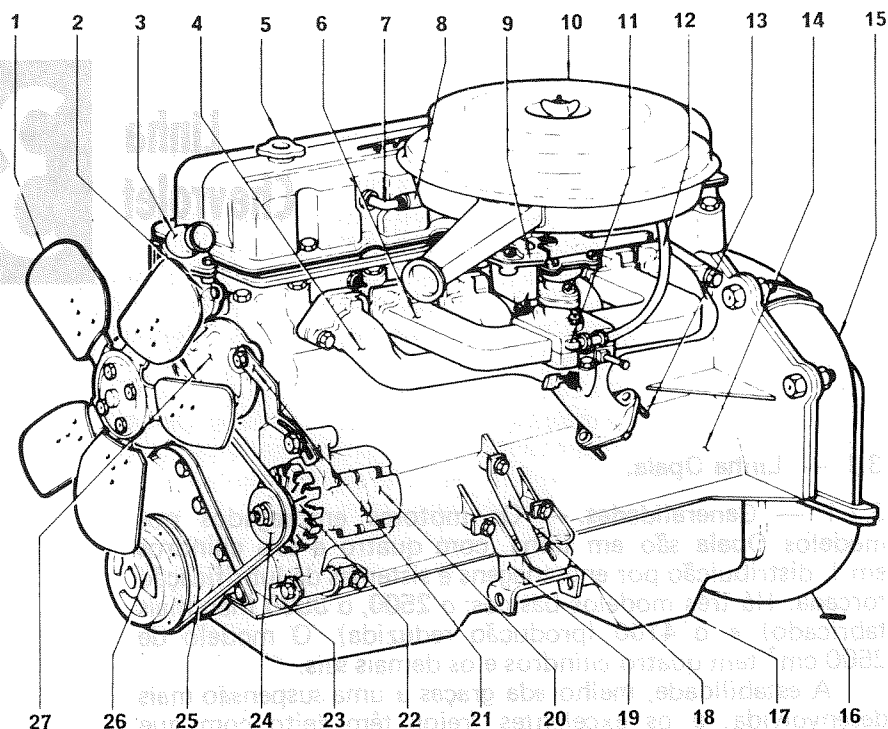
Motor de seis cilindros (vista do lado esquerdo).
